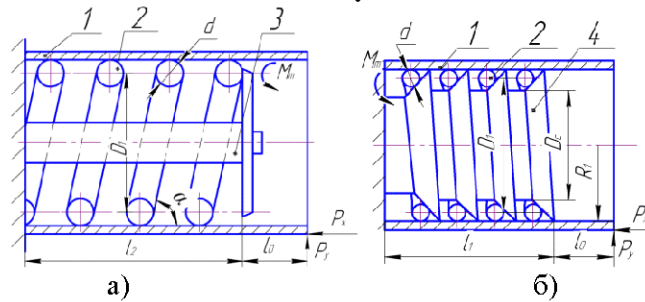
Розрахункові схеми затискних пристроїв: а) без кінчної опори; б) з кінчною опорою 1 - заготовка; 2 – гвинтовий затискний елемент; 3 – тяга; 4 – кінчна опора
